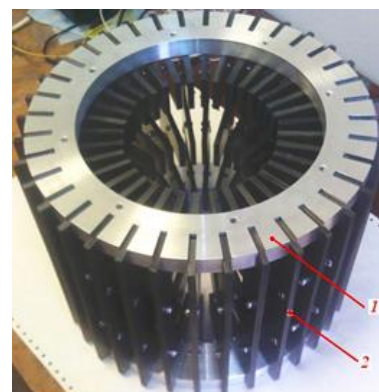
Статор МПСБР:1 – зубцева гребінка, 2 – зубець
